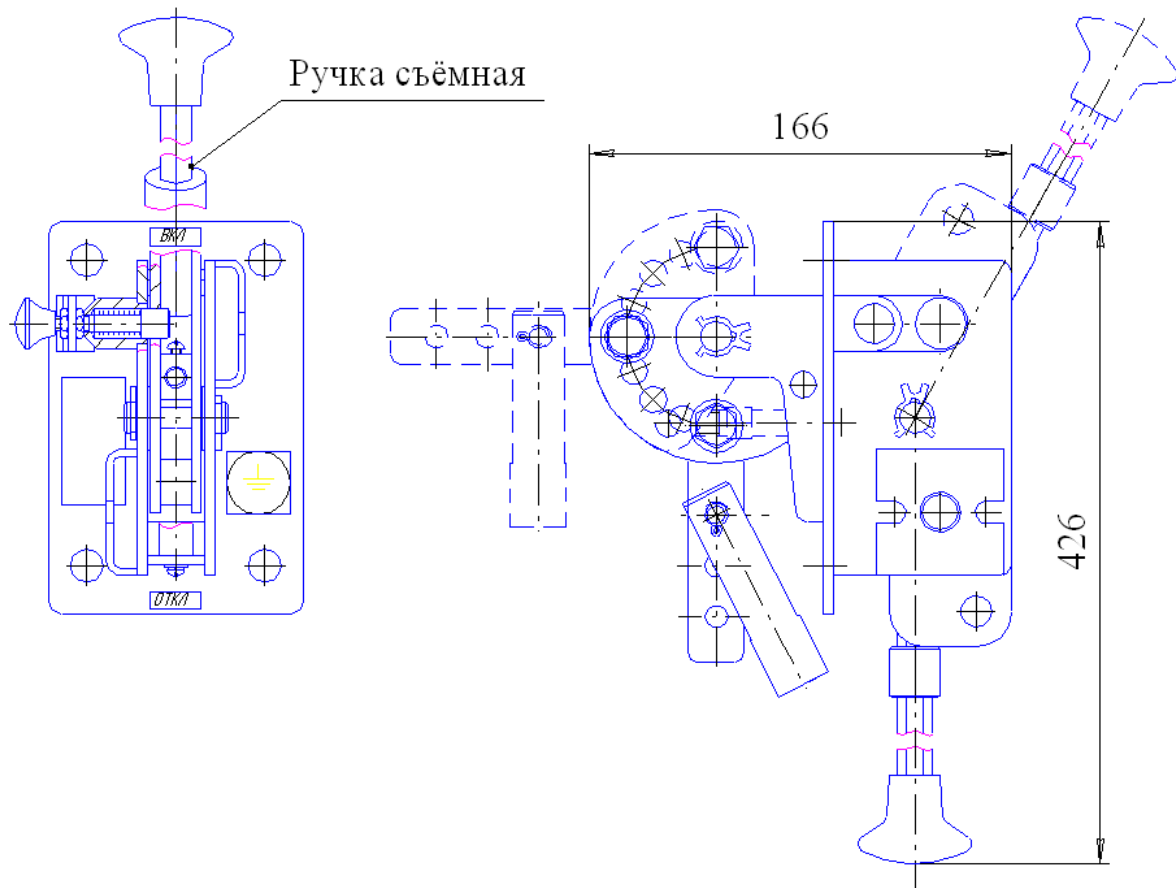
Привод ПРБО-10-У2 (чертеж 6ГК.760.001-01) для ВНА и РВ
